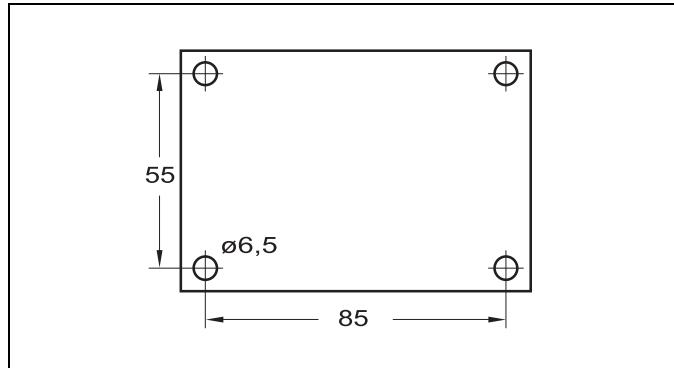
Lochbild für Ständer Umwälzpumpe U 4856
